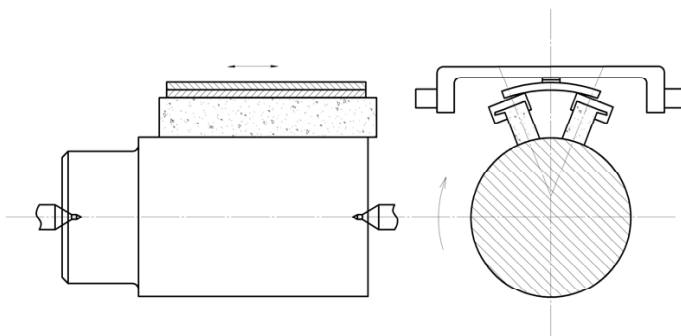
Схема процесса суперфиниширования наружных поверхностей цилиндрических деталей
